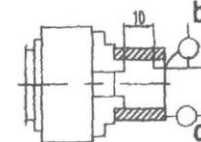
Токарный патрон с креплением заготовки за внутреннюю поверхность с прямыми кулачками
